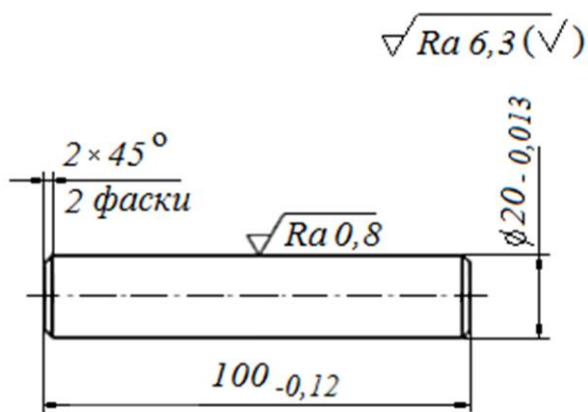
Простановка размеров и параметров шероховатости на чертеже детали
